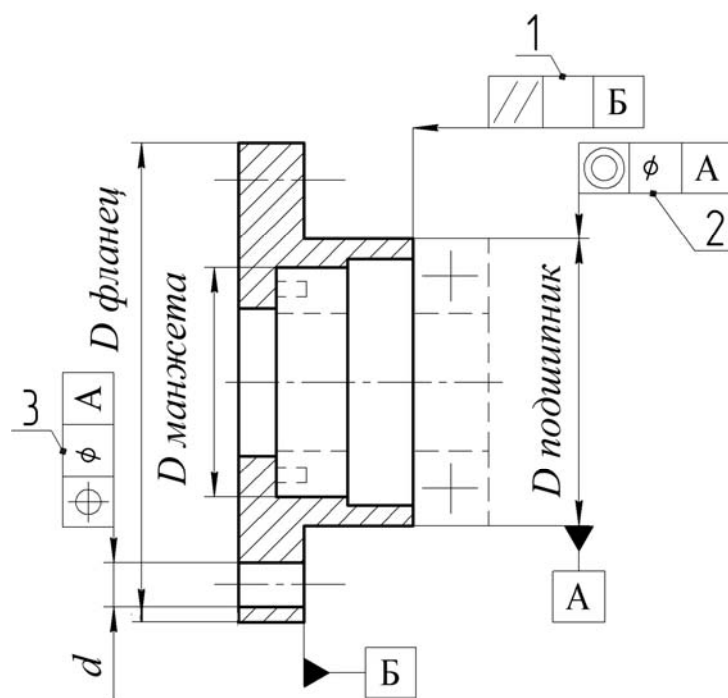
Допуски формы и расположения поверхностей крышки подшипника
